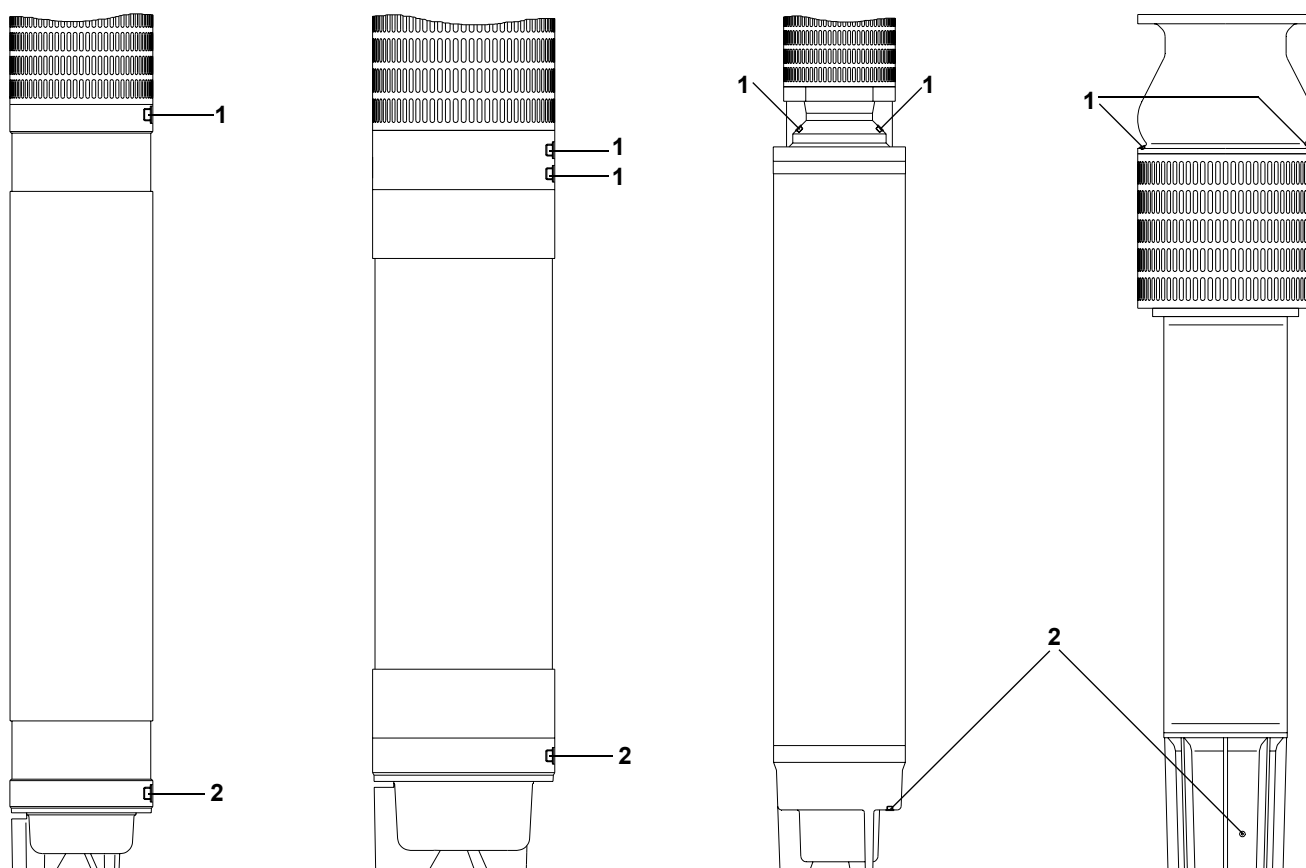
Заливка двигателя, заливное отверстие на корпусе двигателя – вертикальный монтаж
